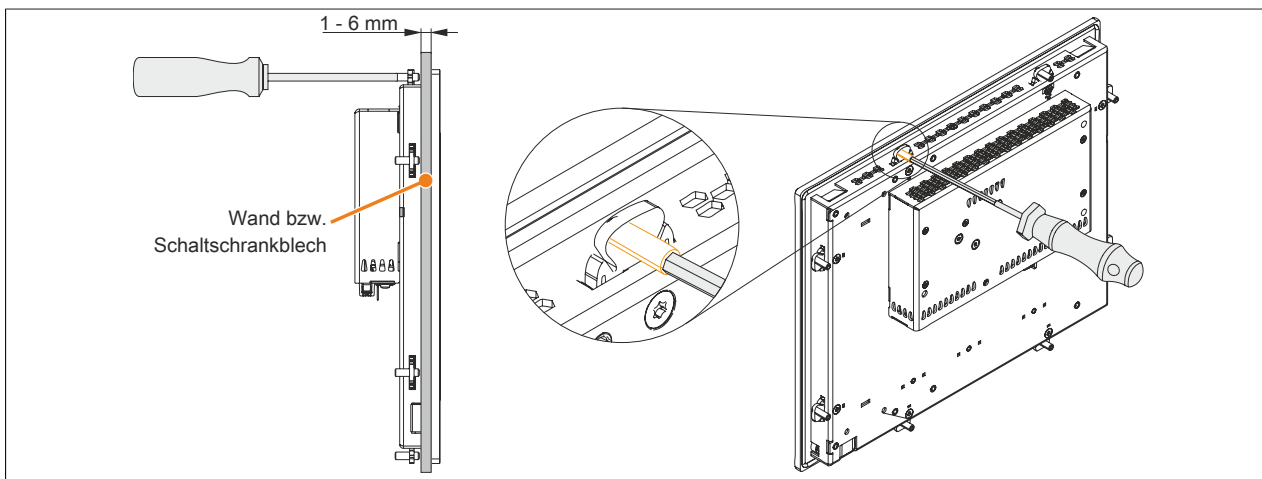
Halteklammern festschrauben (Beispielabbildung)
